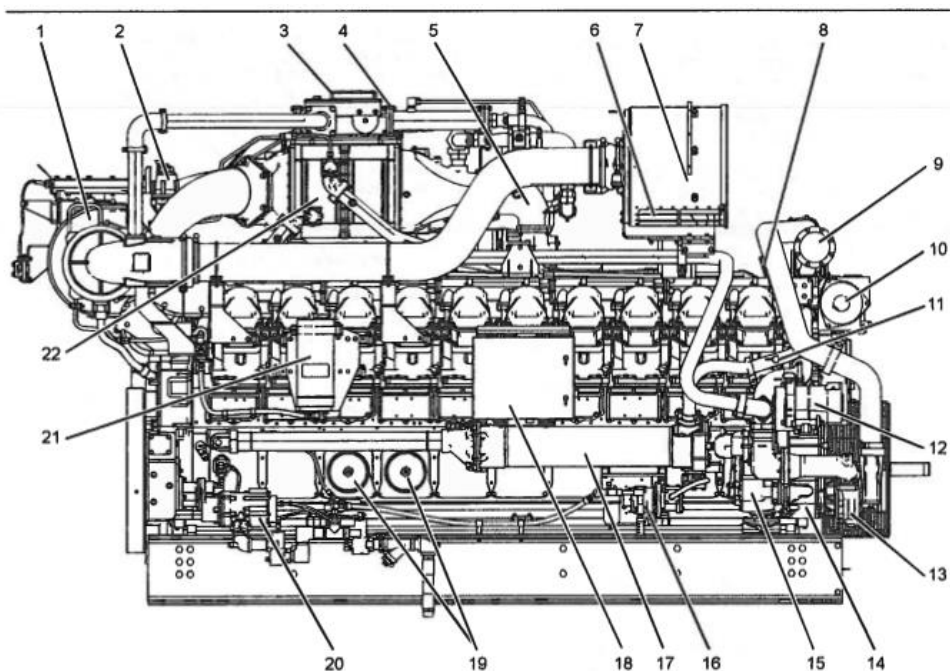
Двигатель CAT3520D вид двигателя справа
